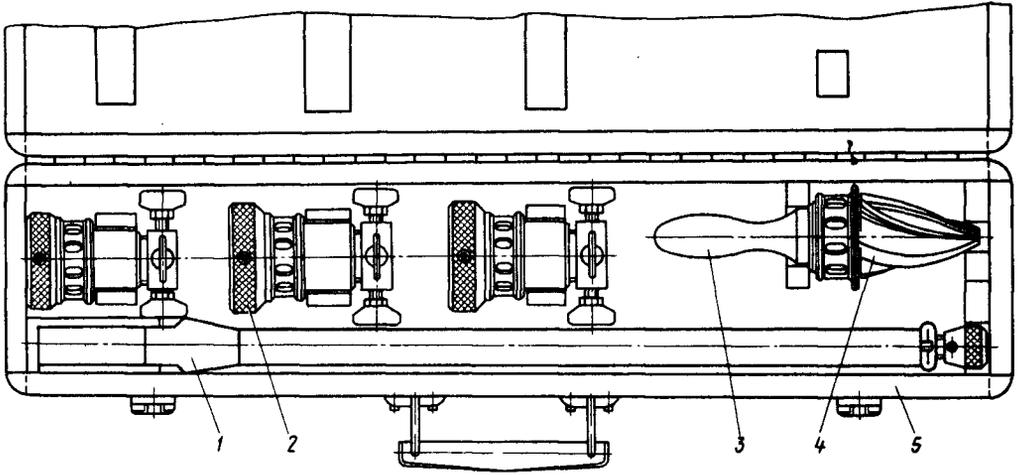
Приспособление ПТС-1 с трещоткой и самозахватом для нарезания резьбы и зенкования труб
